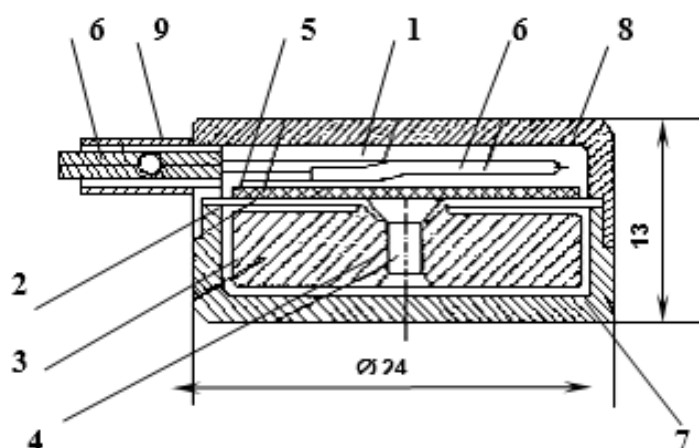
Конструкция акселерометра ПАМТ-1: 1 – пьезопластина (ЦТС-19); 2 – металлическая подложка; 3 – груз; 4 – заклепка; 5 – контактная пластина; 6 – антивибрационный кабель; 7 – корпус; 8 – крышка; 9 – втулка
